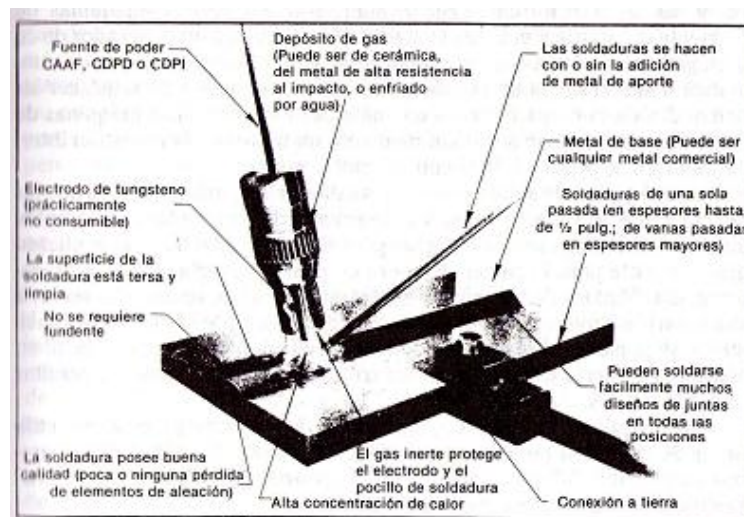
Elementos y aspectos esenciales del proceso de soldadura TIG
